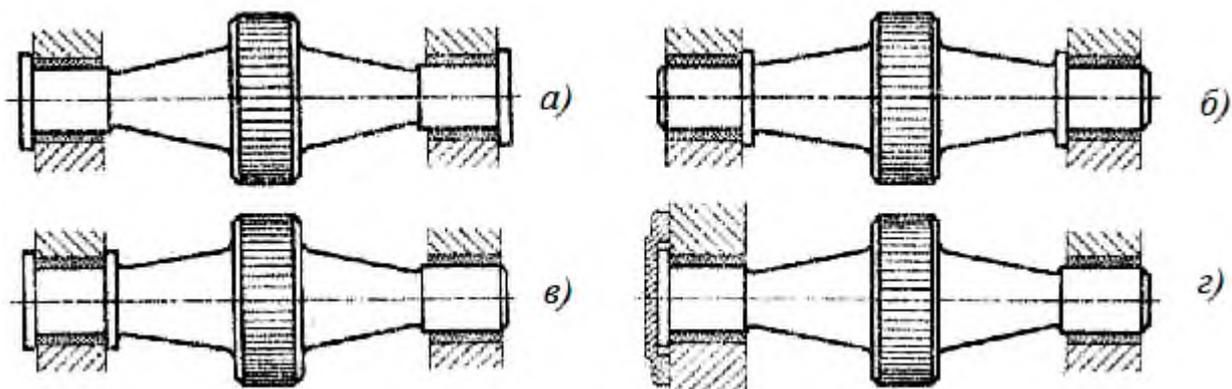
Последовательное улучшение конструкции узла установки вала зубчатого колеса в подшипниках скольжения
